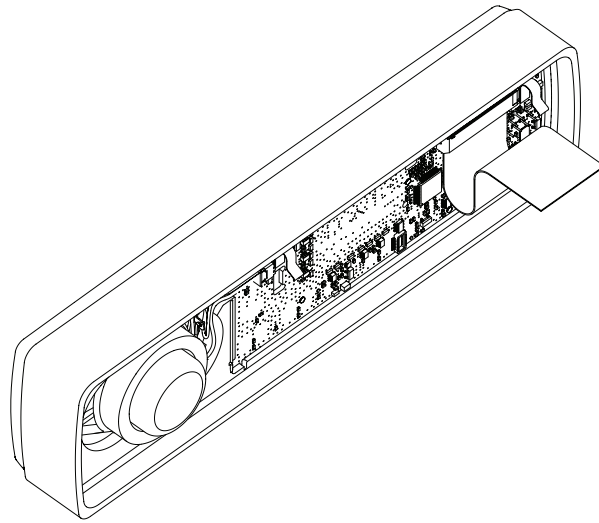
Montagem do Cabo Flexível da Cabeça de Controle à Placa da Cabeça de Controle
